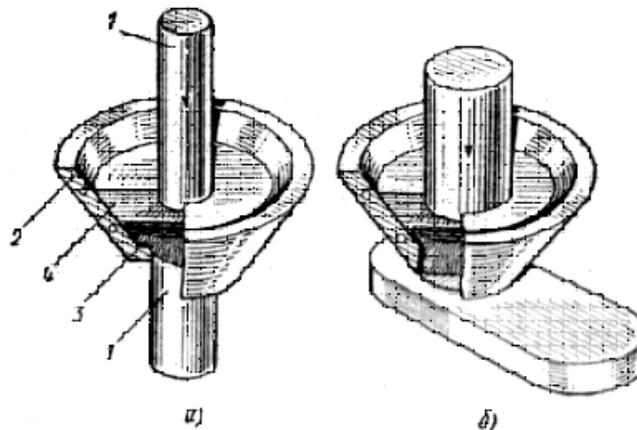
Схема контактно-шлаковой сварки:
